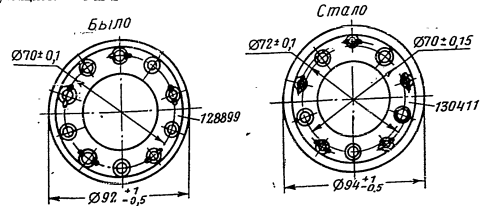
Сателлит валика редуктора двухскоростной передачи нагнетателя. Фиг. 185. Втулка сателлита валика редуктора двухскоростной передачи нагнетателя.
